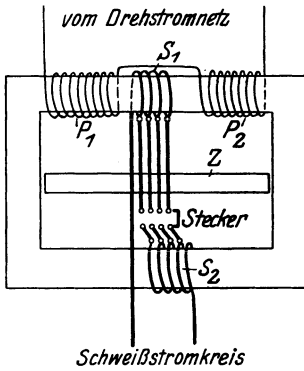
Schweißtransformator mit Streupaketen.
